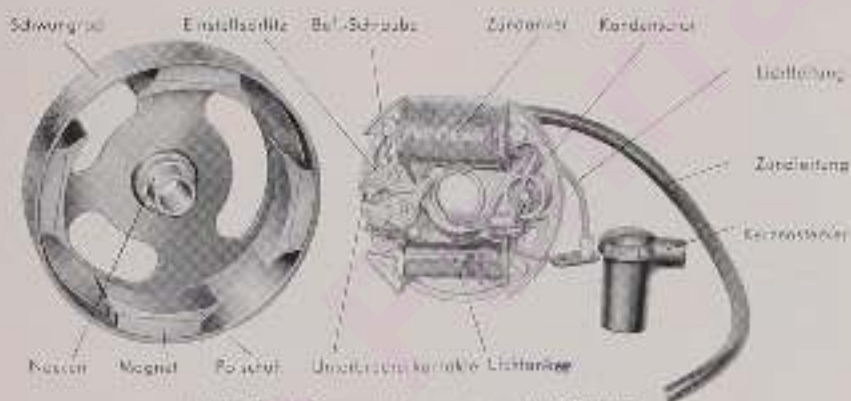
Bosch-Schwungradmagnetzunder LM/UPA 1/115
